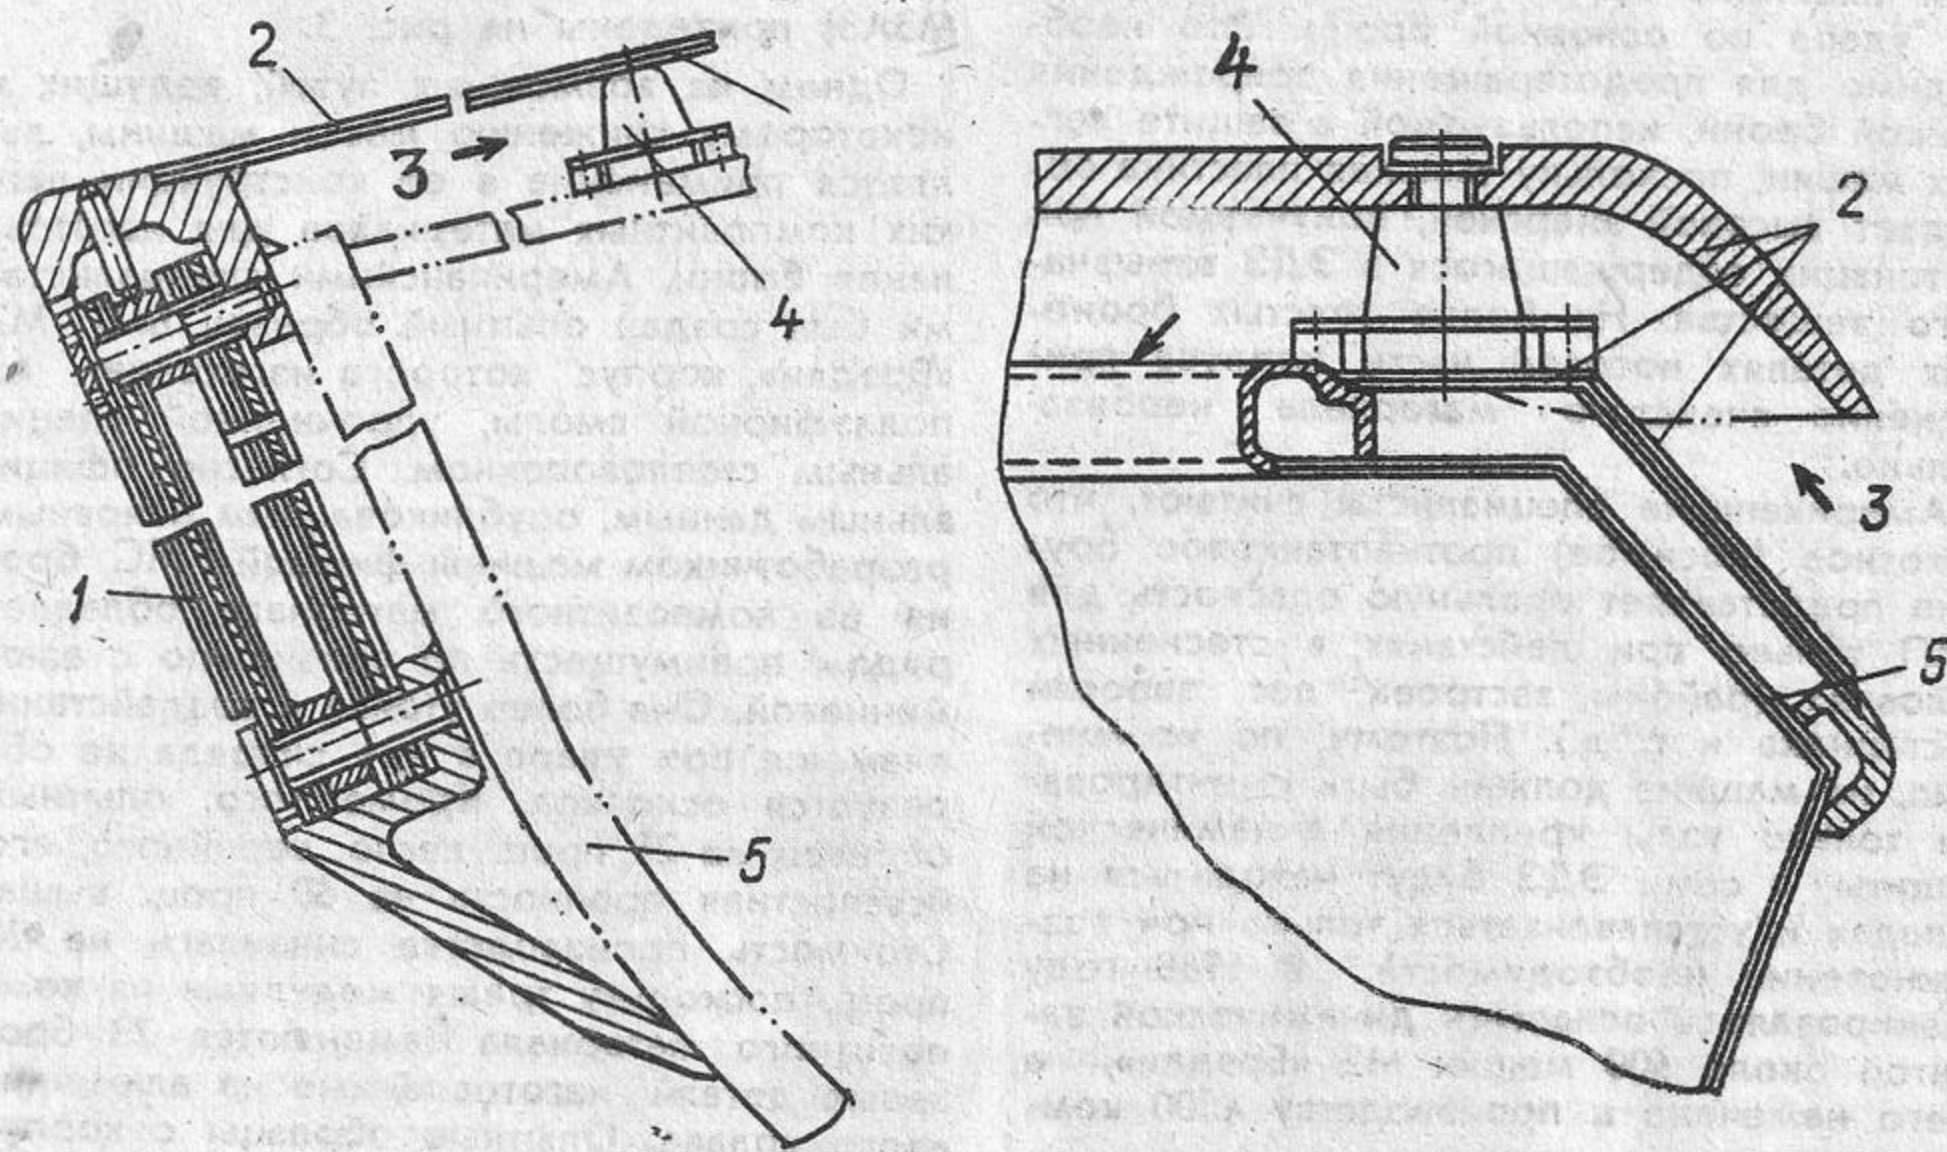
Схема дополнительного бронирования носового узла (слева) и крыши (справа) корпуса: 1 — броневые листы для усиления нижней лобовой части корпуса; 2 — верхние дополнительные броневые листы; 3 — полости прохода воздуха; 4 — опоры крепления броневых листов; 5 — основная броня
